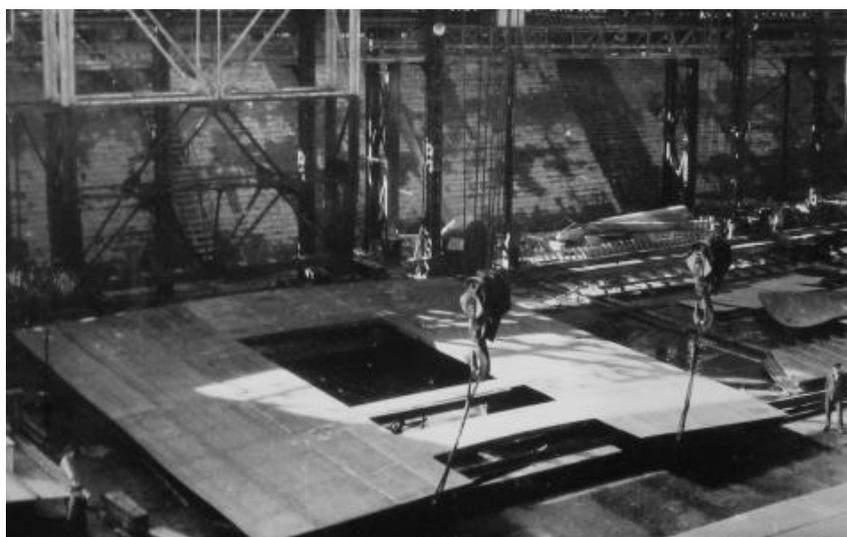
Panneau de pont d'un cargo de 2 600 tonnes
